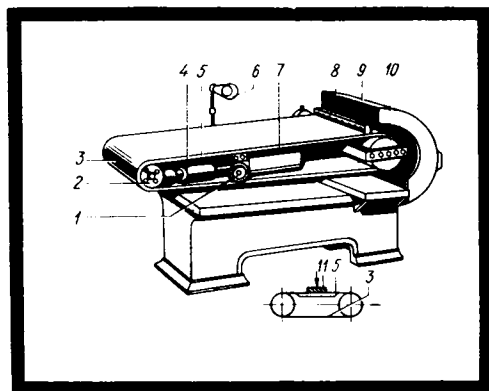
Ленточно-шлифовальный станок с неподвижным столом ШлНСВ:
